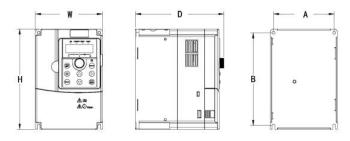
300 系列 塑胶结构外型尺寸及安装尺寸示意图
